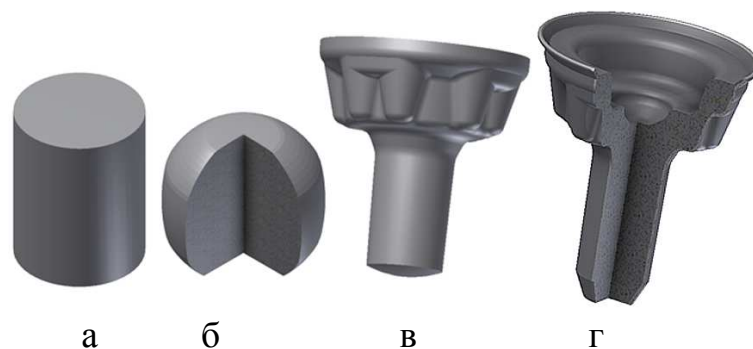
Технологические переходы штамповки изделия: а – заготовка, б – осадка (в шар), в – предварительная штамповка, г – окончательная штамповка
